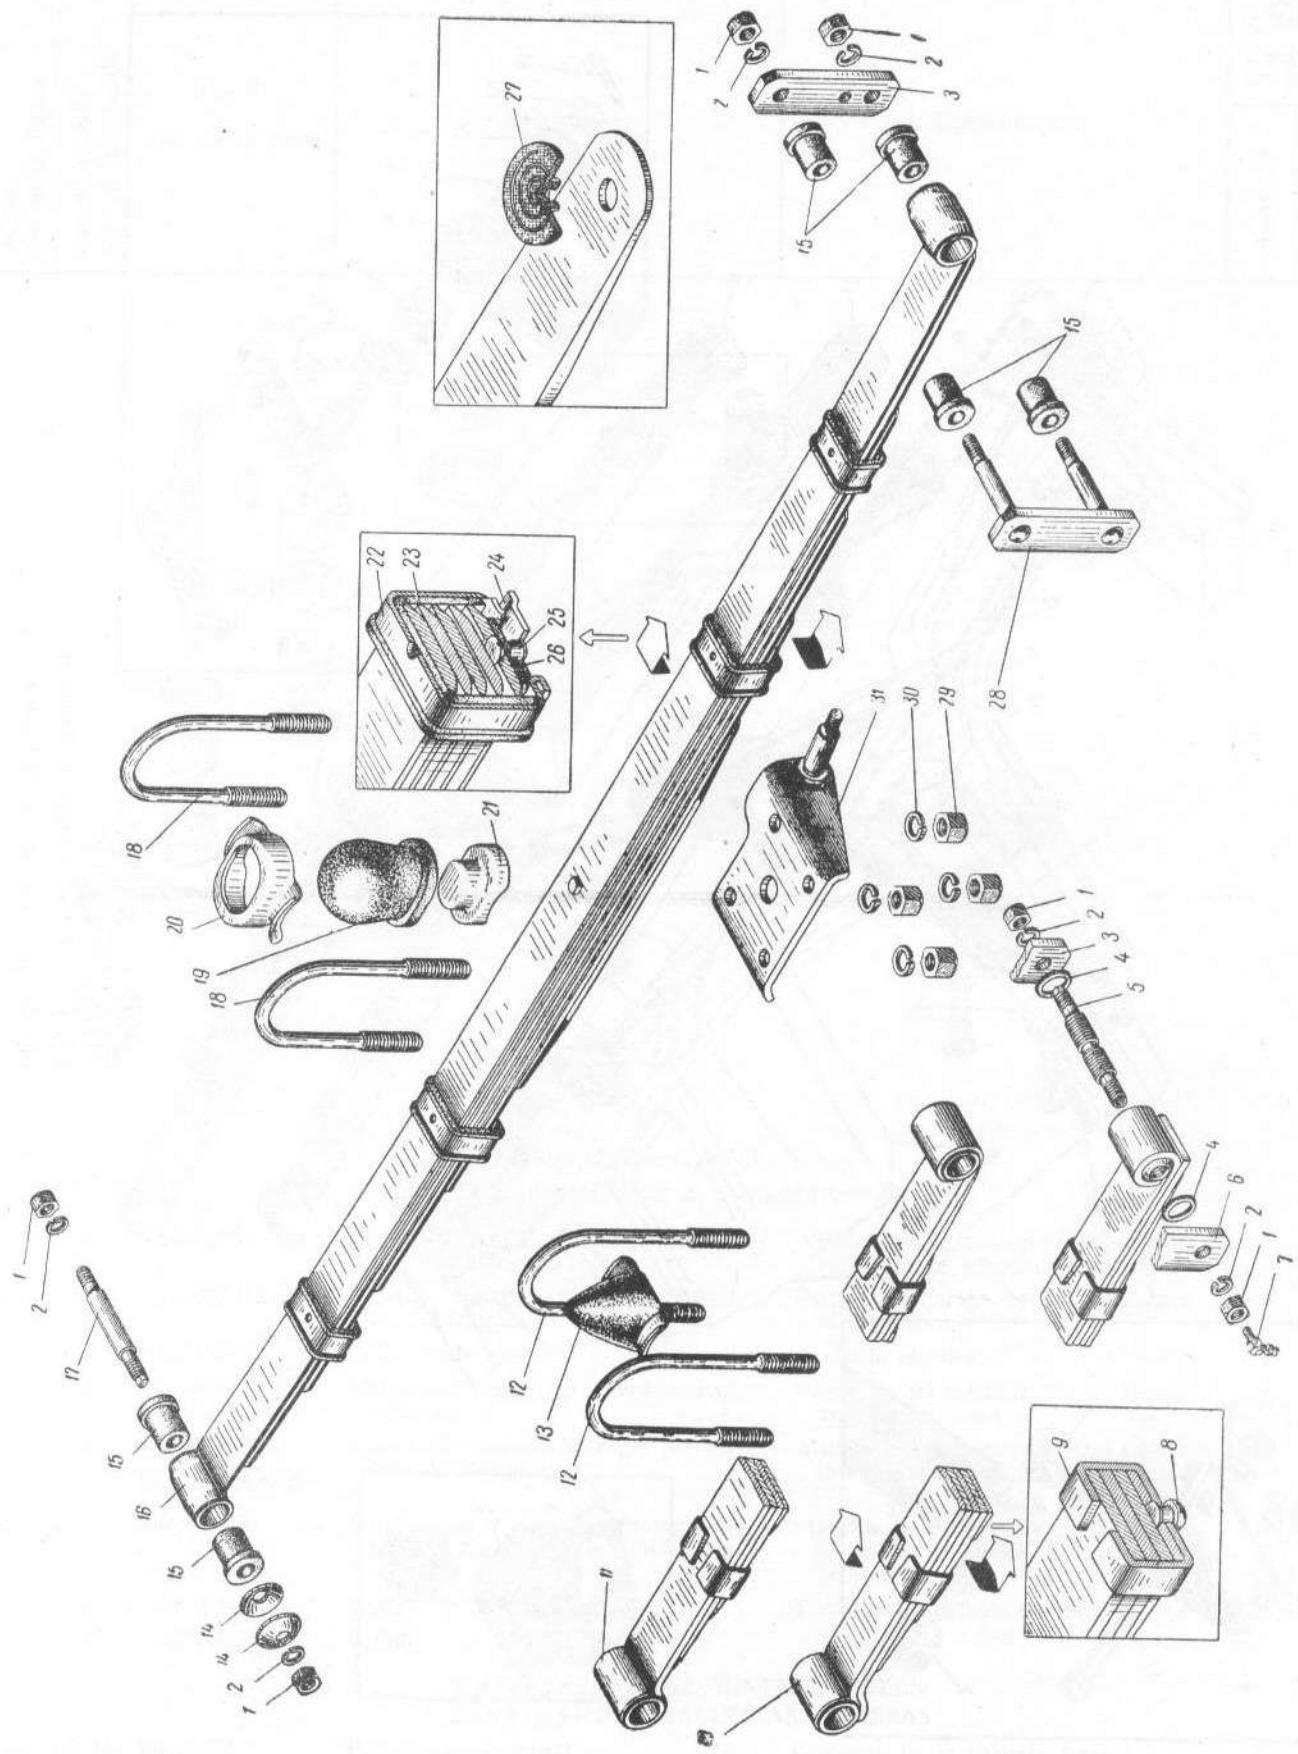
Blattfeder der Hinterradaufhängung mit Befestigungsteilen
